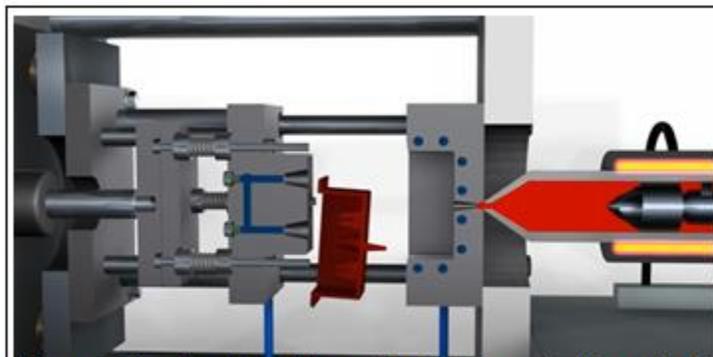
Apertura de molde y obtención de producto terminado a partir de moldeo por inyección.
